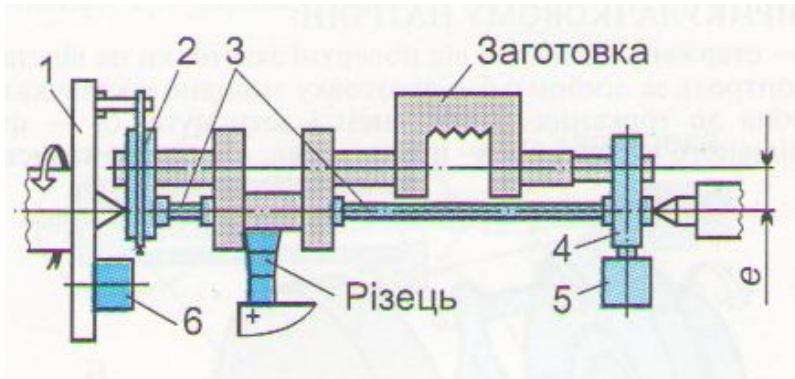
Обробка колінчастого вала із застосуванням центрозміщувальних шайб:
